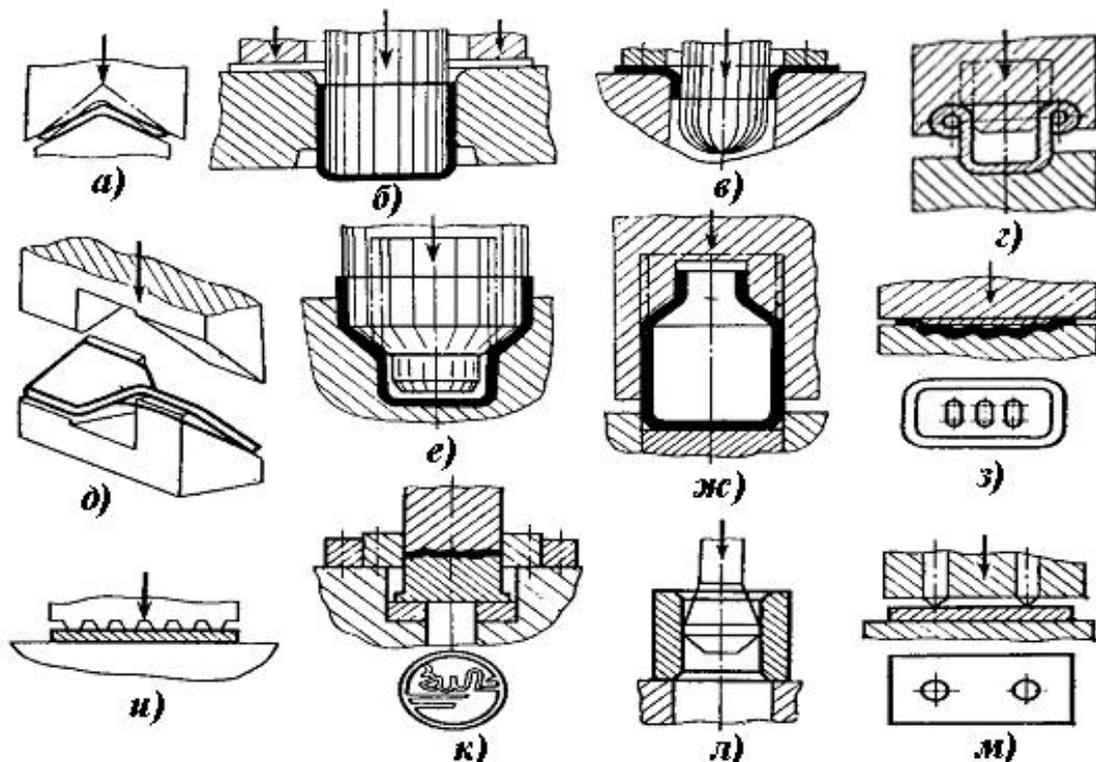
Формообразующие операции листовой штамповки: гибка (а), вытяжка (б), отбортовка (в), закатка (г), скручивание (д), раздача (е), обжим (ж), формовка (з), правка (и), чеканка (к), калибровка (л), кернение (м)
